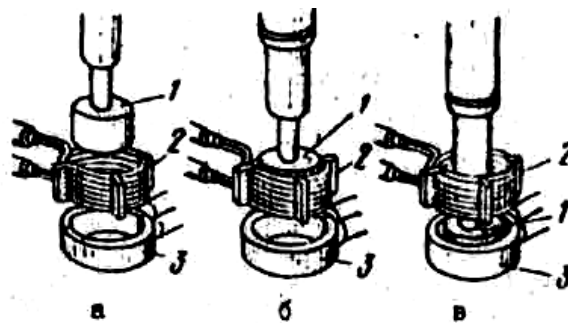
Закалка цилиндрической детали с нагревом ТВЧ:
